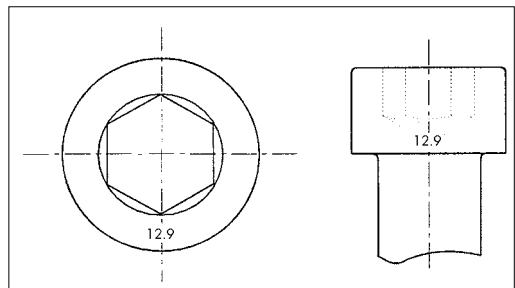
Abb. H: Beispiel für die Kennzeichnung von Zylinderschrauben mit Innensechskant
